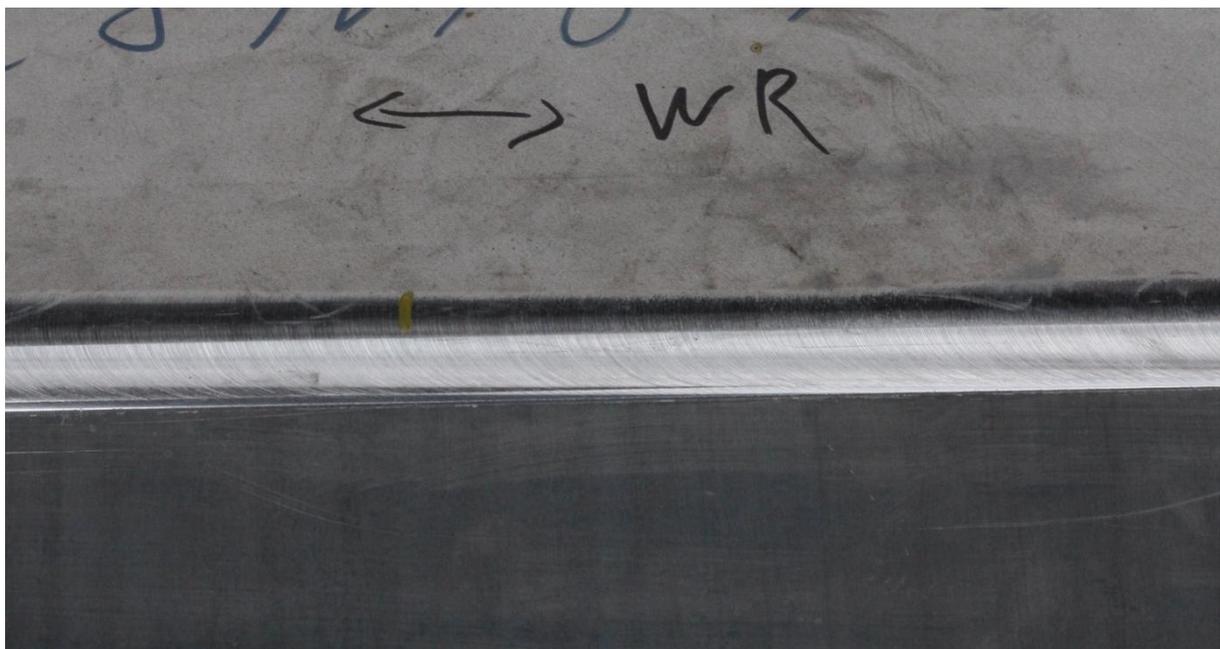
Aluminium/Stahl-Verbindung (oberhalb der Schweißnaht CrNi-Stahl)
